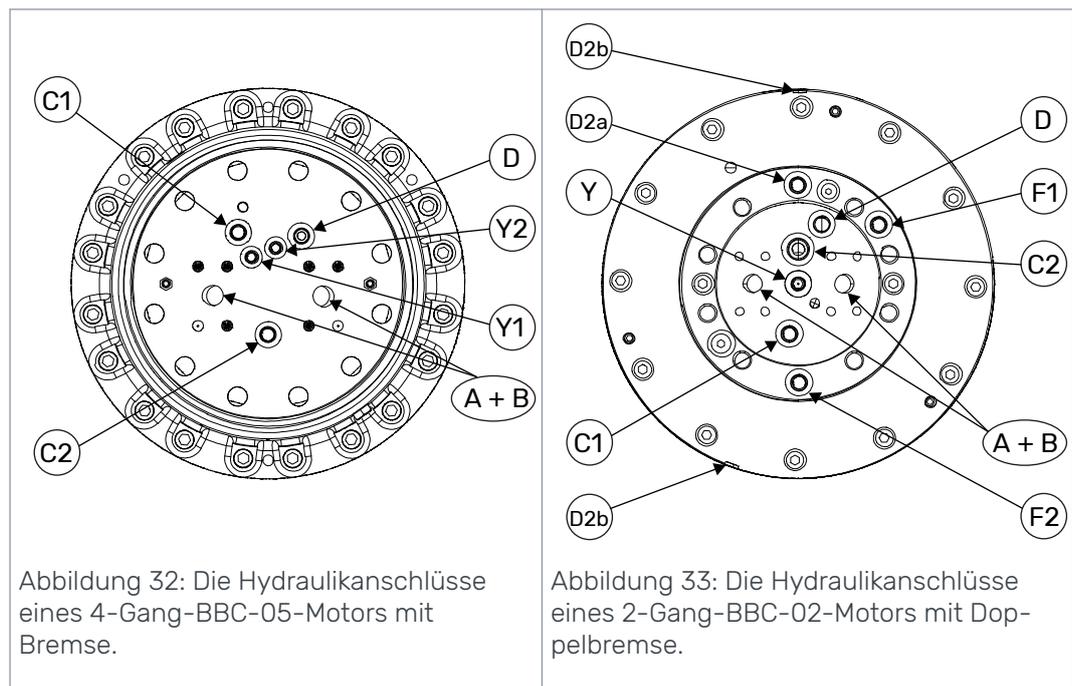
Die Hydraulikanschlüsse eines 4-Gang-BBC-05-Motors mit Bremse.
